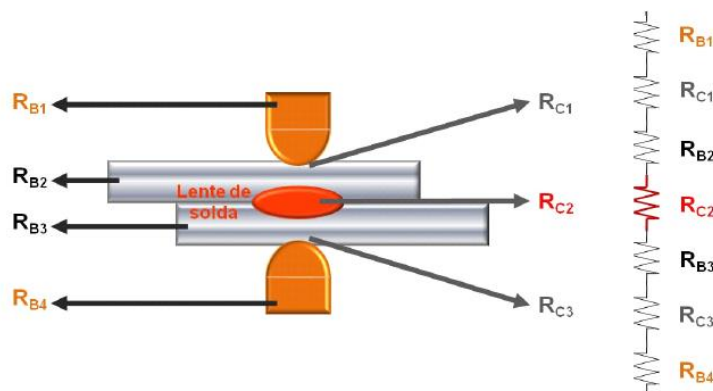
Representação de todas as resistências presentes na soldadura por pontos
